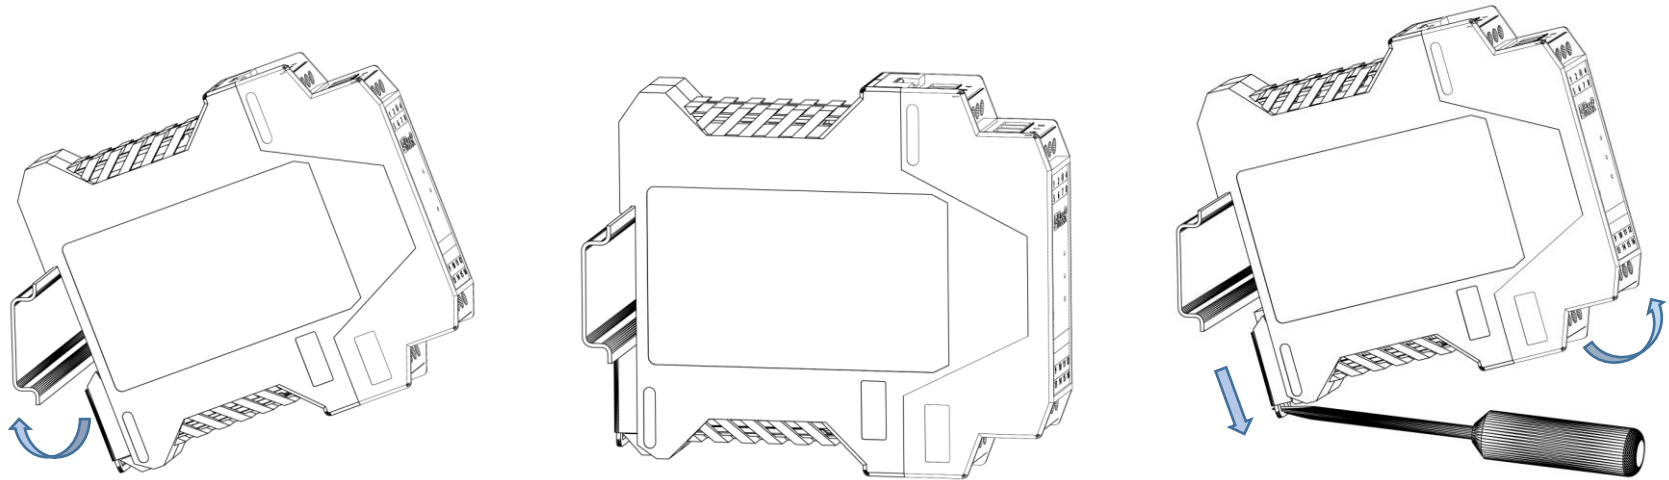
Montaggio-smontaggio meccanico / Mechanical assembly-disassembly
